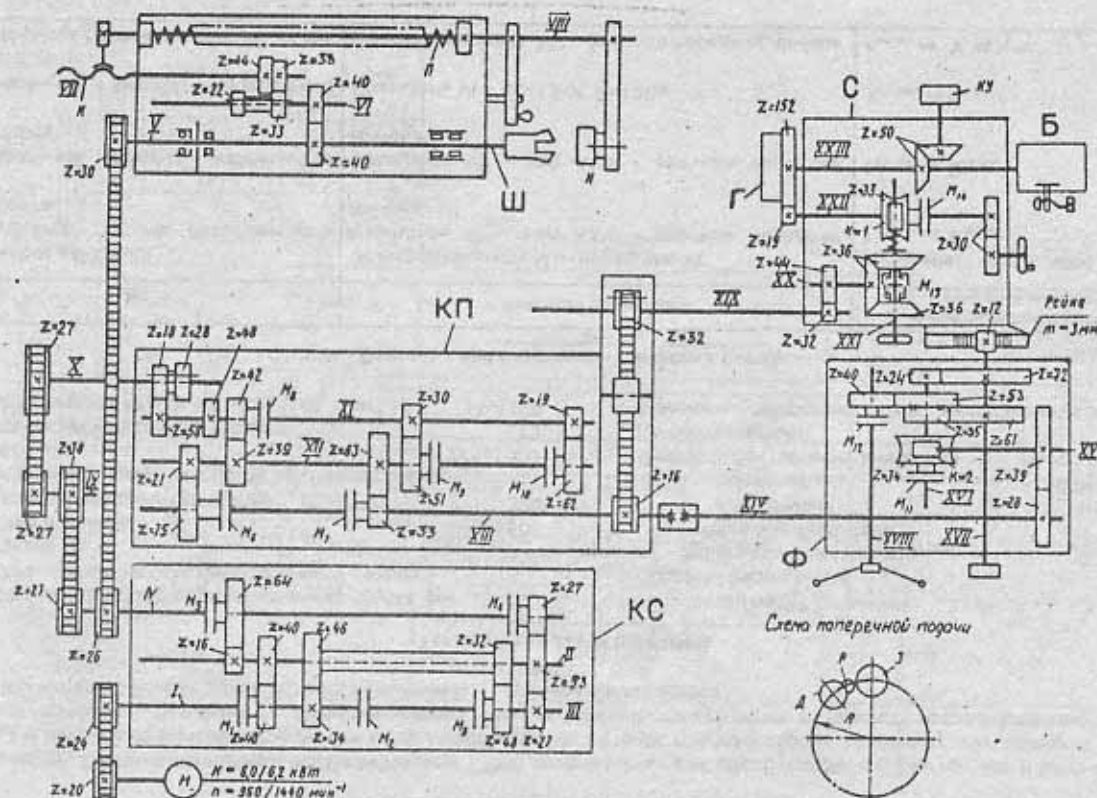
Кинематическая схема токарно-револьверного станка мод. 1Г340
